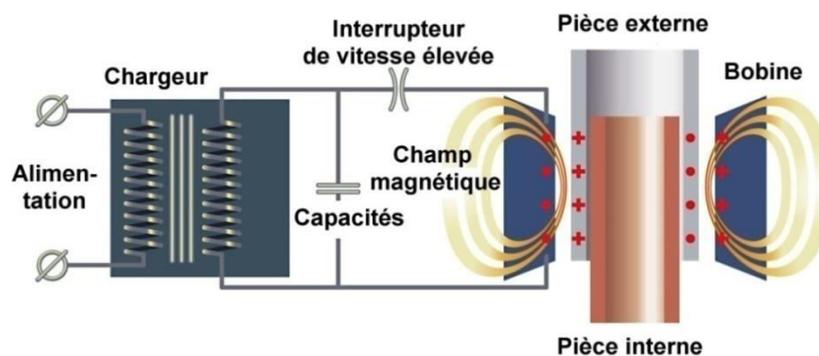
Principe du soudage par impulsion magnétique.
